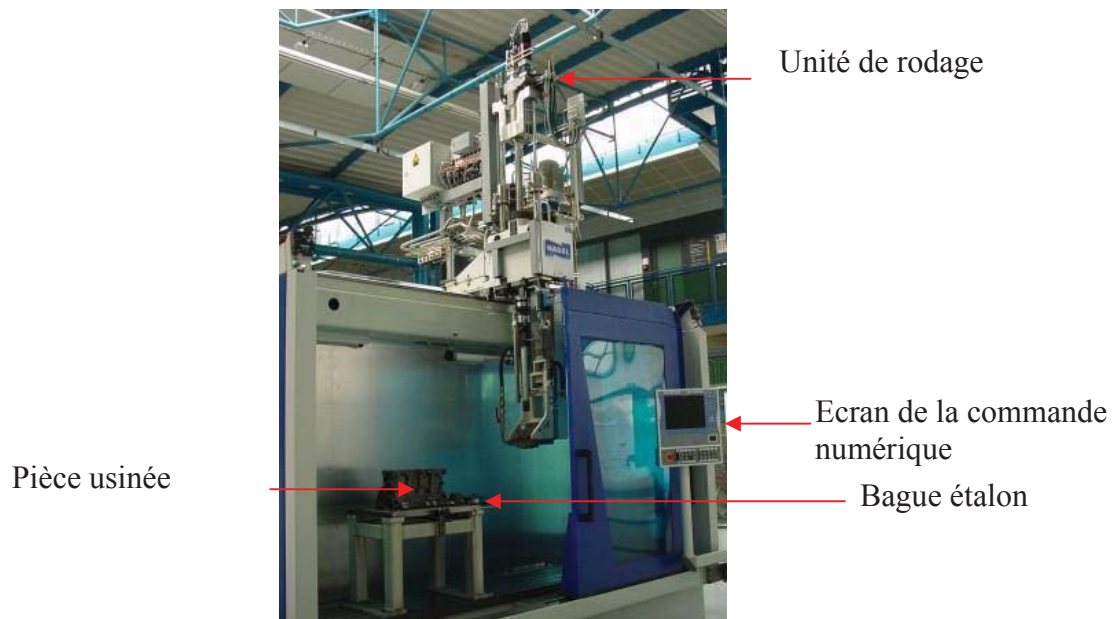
Vue d'ensemble du banc de rodage à l'échelle 1
